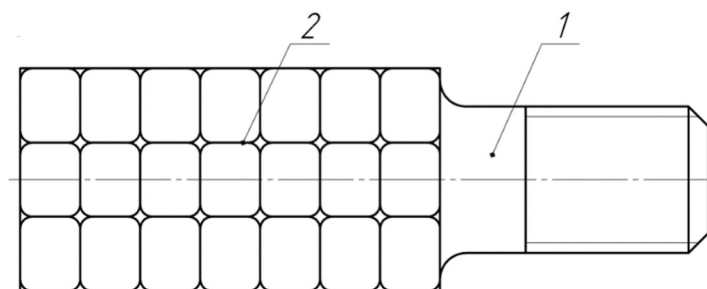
Схема наплавки на рабочей поверхности била: 1 – било, 2 – сетка прямоугольной формы
